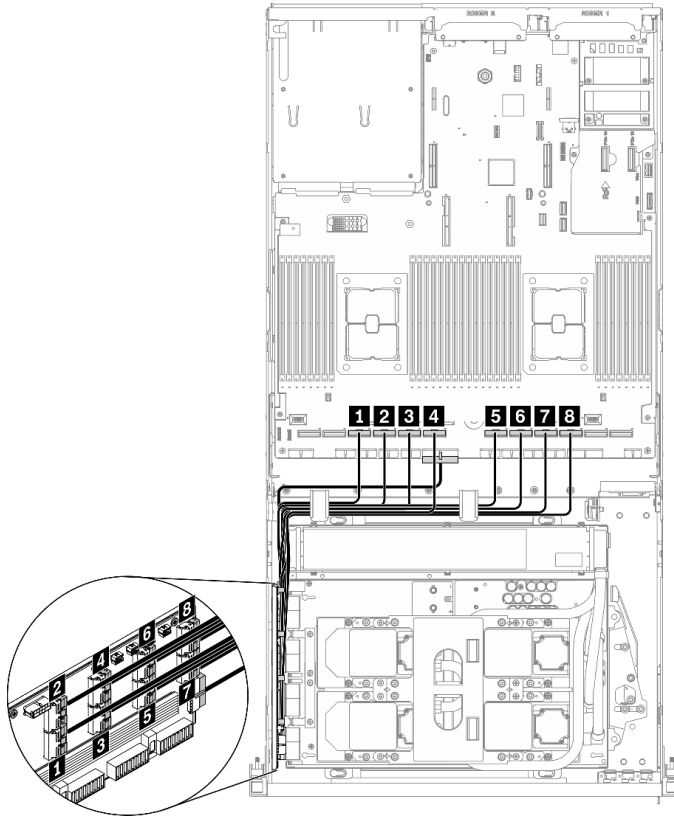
Disposición de los cables del conjunto de retemporizador (cables de señal): Configuración F
